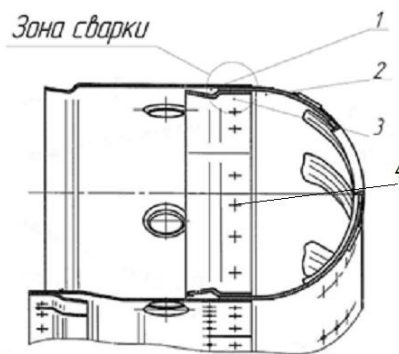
Жаровая труба, 1 – Стенка наружная, 2 – Головка, 3 – Экран наружный, 4 – Сварные точечные соединения
